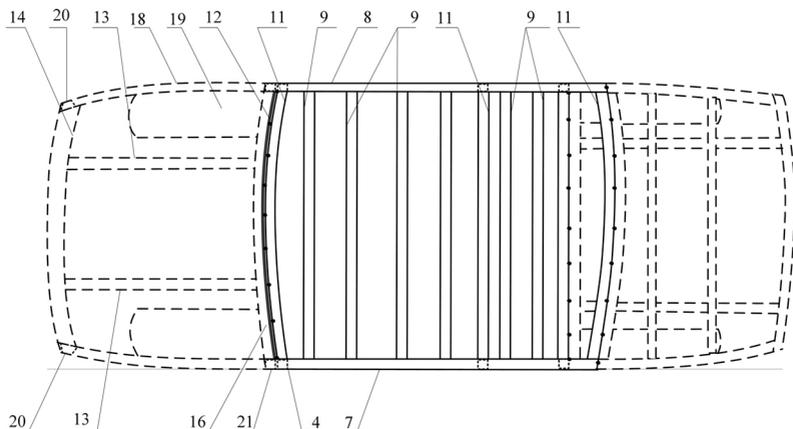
Общий вид каркаса автомобиля сверху: 4 – передние стойки; 7 – пороги; 8 – продольные балки крыши; 9 – поперечные нижние балки; 11 – верхние балки; 12 – передний щит; 13 – лонжероны; 14 – поперечные передние верхние балки; 16 – поперечные задние верхние балки; 18 – балки; 19 – арки крыльев; 20, 21 – передние и задние стойки
